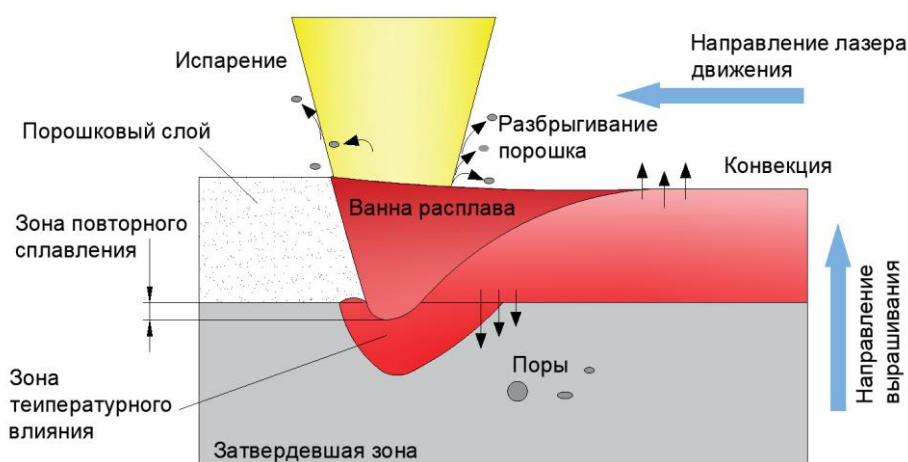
Схематическое представление лазерного сплавления порошкового слоя
